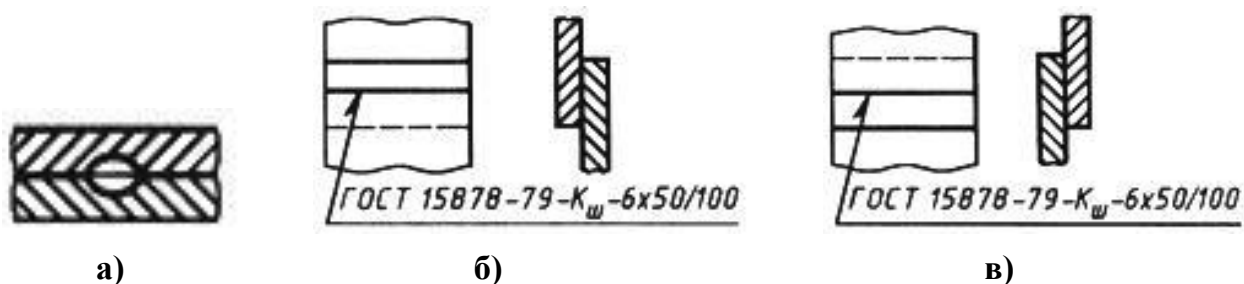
Пример обозначения сварного шва [5]: а – форма поперечного сечения шва; б – обозначение с лицевой стороны; в – обозначение с оборотной стороны
